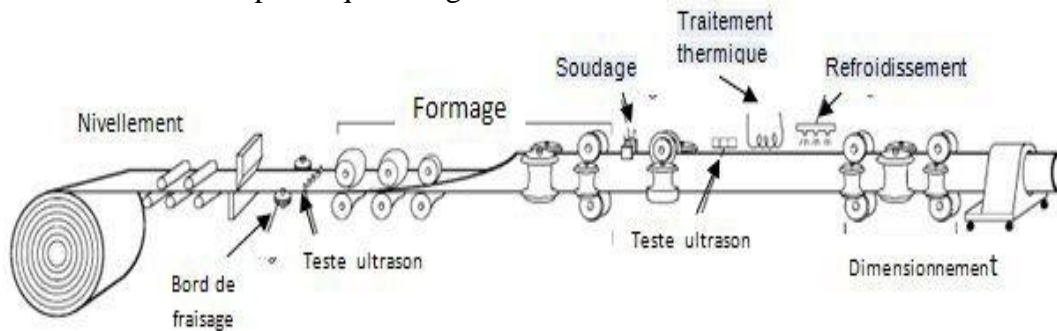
Technique de fabrication des tubes soudés en spirale
